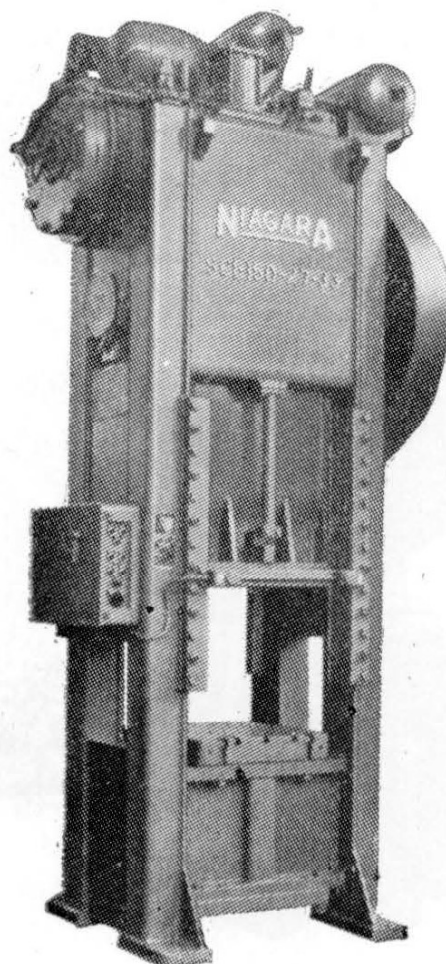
Prensa (Niagara Machine & Toolworks).
